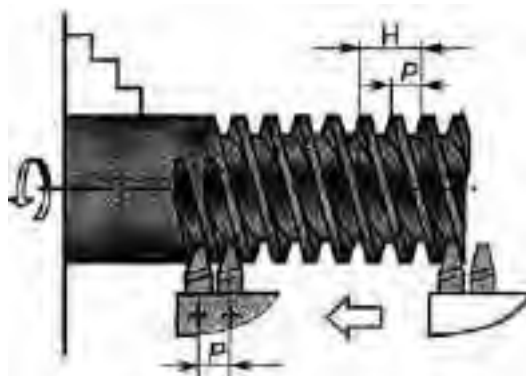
СХЕМА НАРІЗУВАННЯ ДВОЗАХІДНОЇ РІЗЬБИ ДВОМА РІЗЦЯМИ
